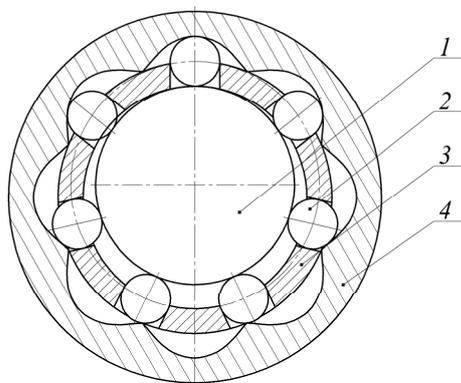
Основные элементы планетарно-волновой передачи зацеплением с промежуточными телами: 1 – генератор волн с одним периодом профиля (подшипник качения не показан); 2 – промежуточные тела; 3 – сепаратор; 4 – профильное колесо
